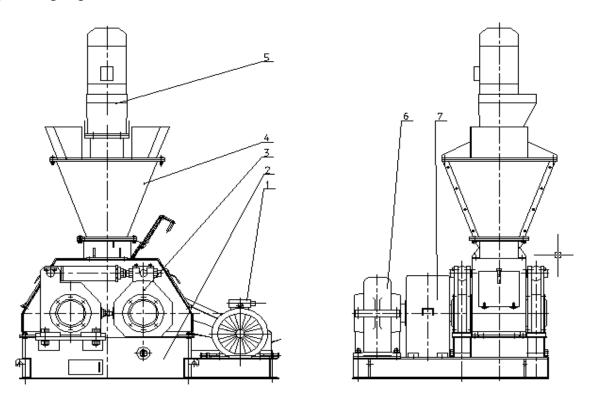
Схема валкового пресса с подпрессовщиком для гранул: 1 – привод на базе электродвигателя; 2 – рама; 3 – подвижный валок; 4 –шнековый подпрессовщик; 5 – привод подпрессовщика; 6 – цепная передача; 7 – зубчатая пара
